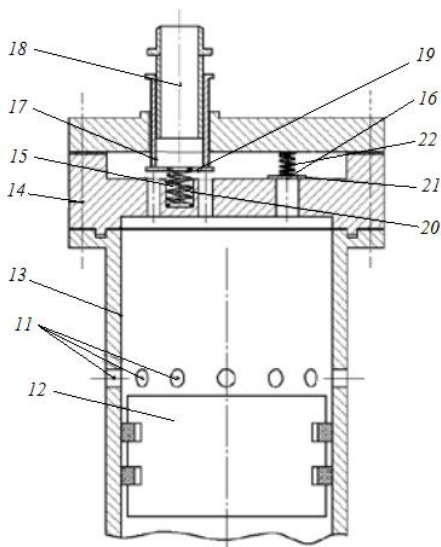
Поршневий пневмодвигун з автоматичними клапанами гібридної силової установки: 11 – вихлопні вікна; 12 – поршень; 13 – циліндр; 14 – кришка циліндра; 15 – впускний клапан; 16 – випускний клапан; 17 – впускний штуцер; 18 – обмежувач підйому; 19, 21 – запірний елемент; 20, 22 – пружина
